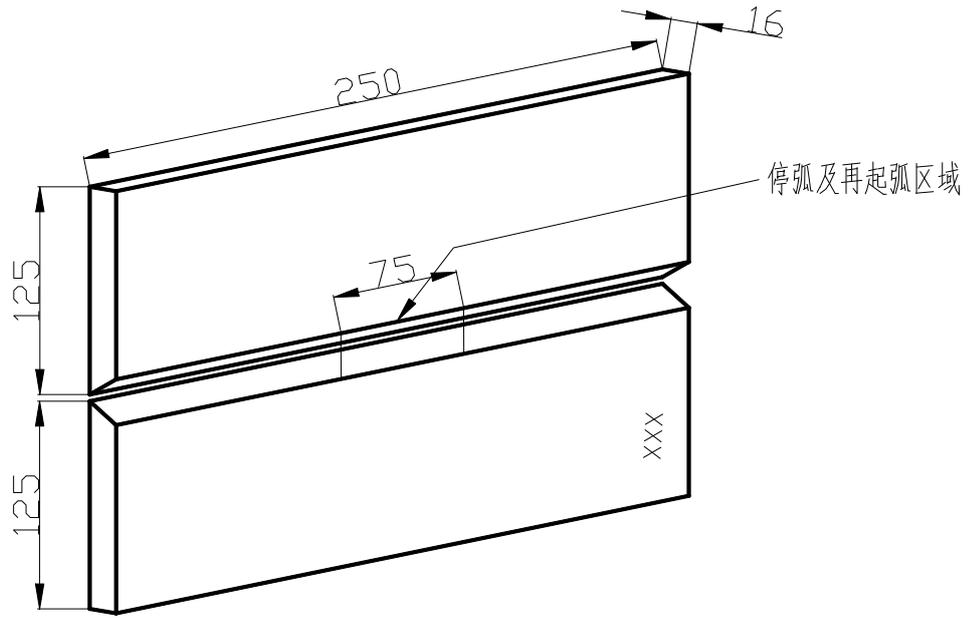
板对接二氧化碳气体保护焊实芯焊丝横焊
